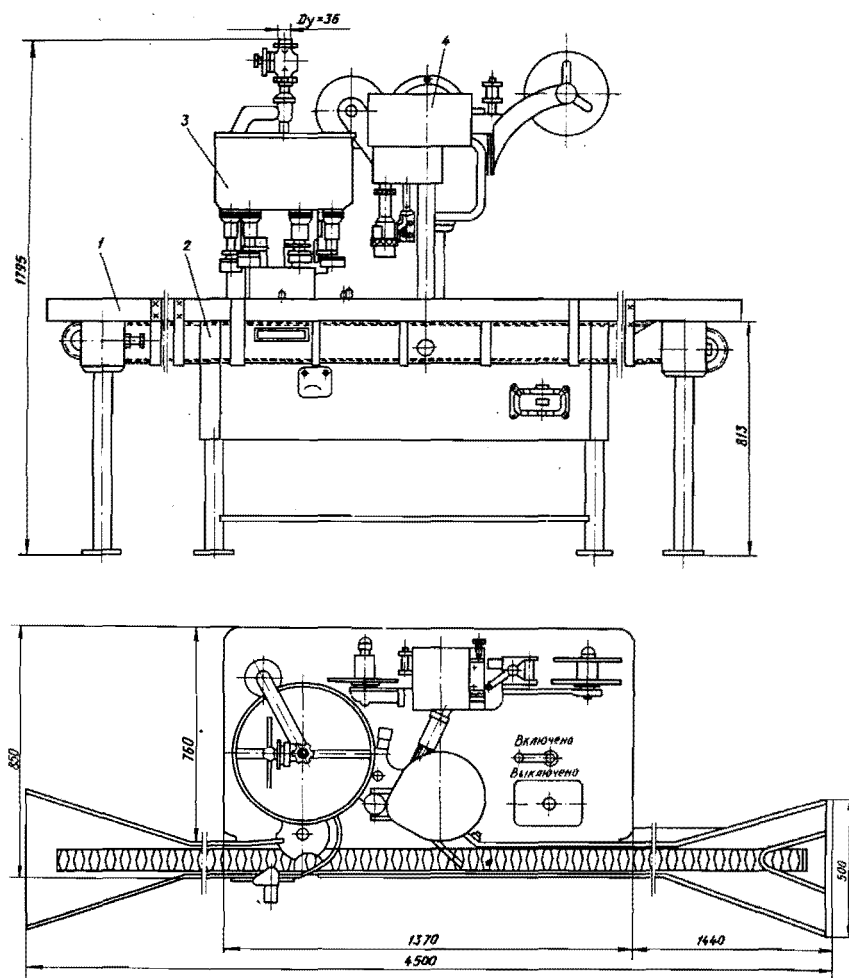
Общий вид автомата разливочно-укупорочного марки АРУ-М:
